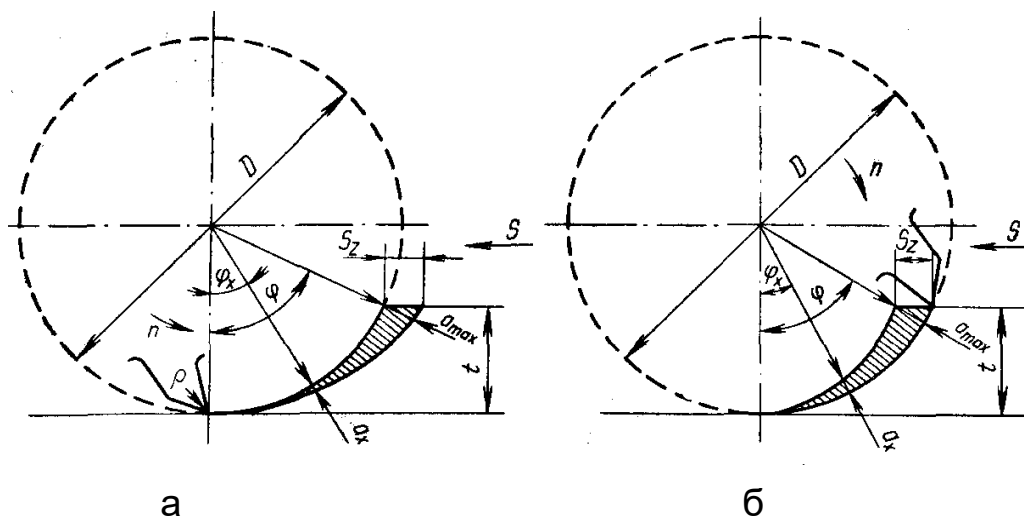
Схемы резания при встречном (а) и попутном (б) цилиндрическом фрезеровании
